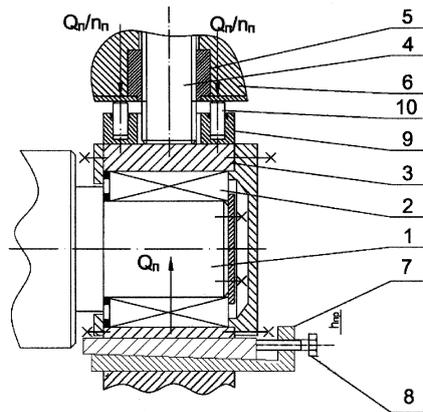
Предлагаемая конструкция комбинированного гидромеханического нажимного механизма чистовых рабочих клетей станов для горячей прокатки сортовых полосовых и ленточных заготовок
